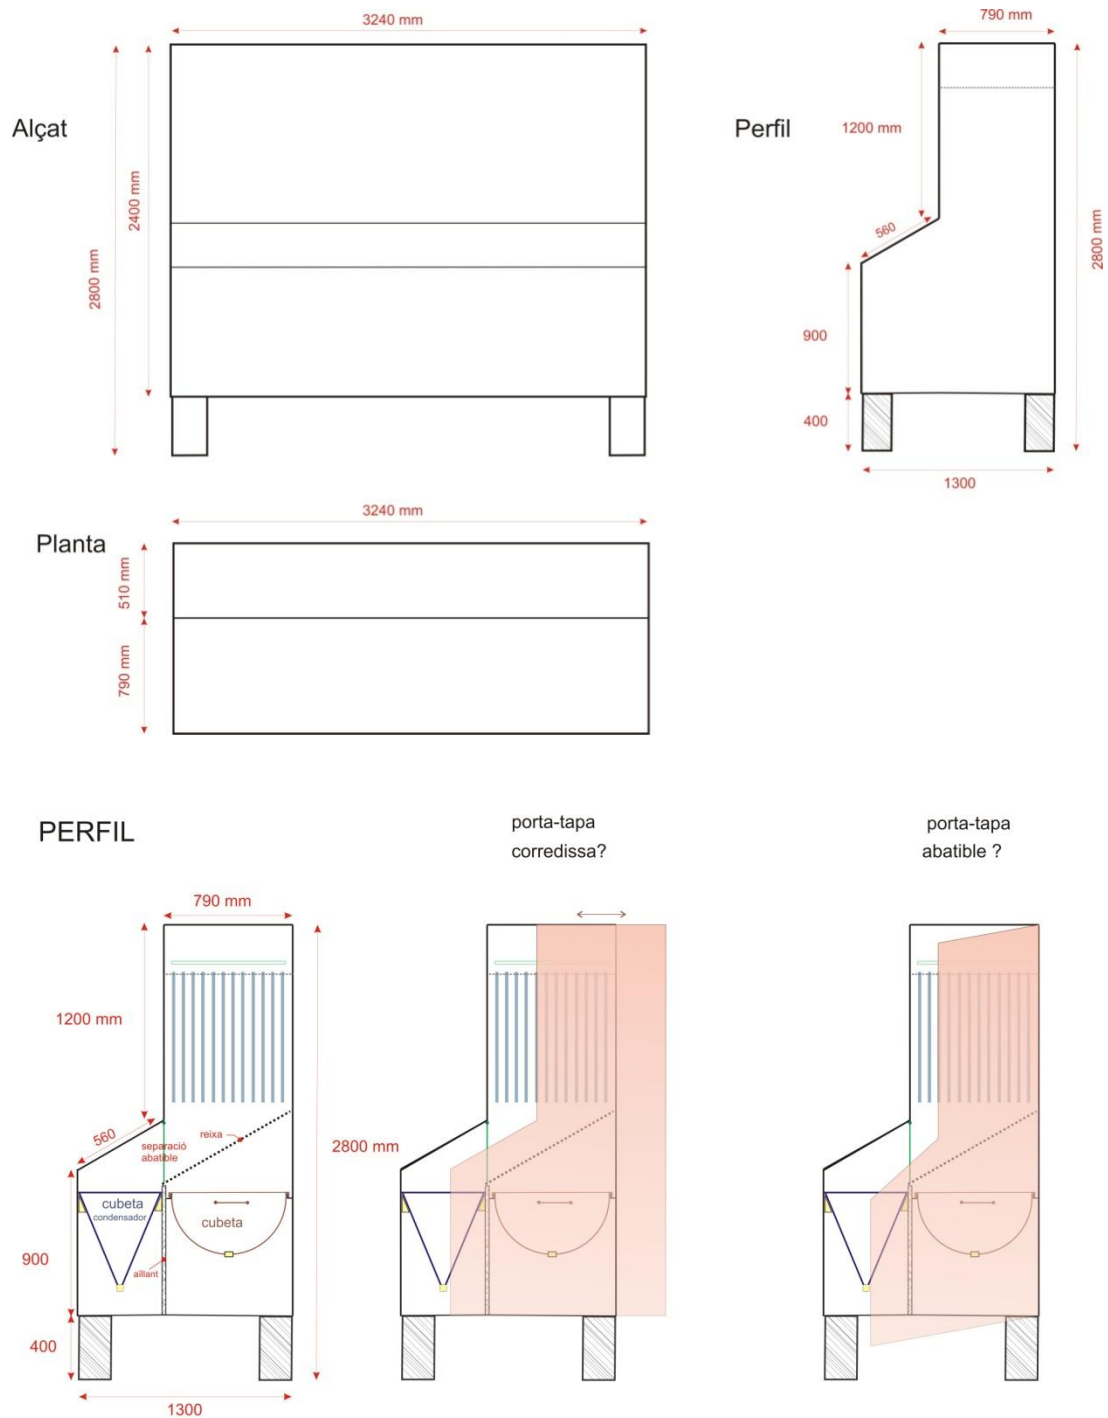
Vistes: planta, alçat i perfil de las cambres. Elaboració pròpia.
